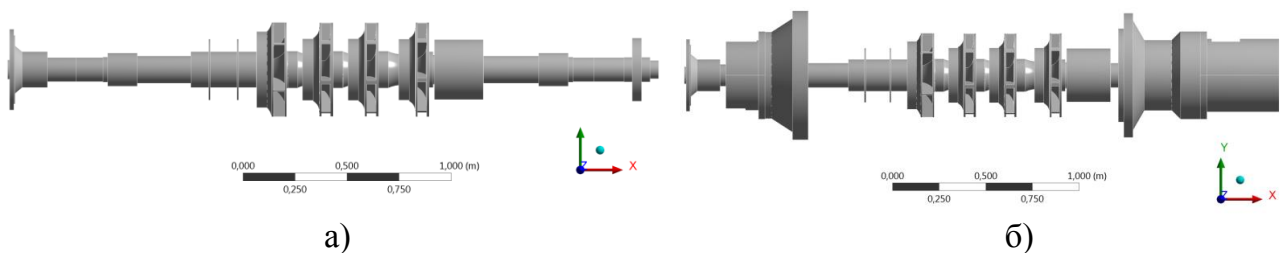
Геометрична модель ротора: а) без корпусів підшипникових опор; б) з корпусами підшипникових опор
